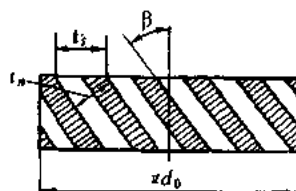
斜齿圆柱齿轮的分度圆柱面展开
